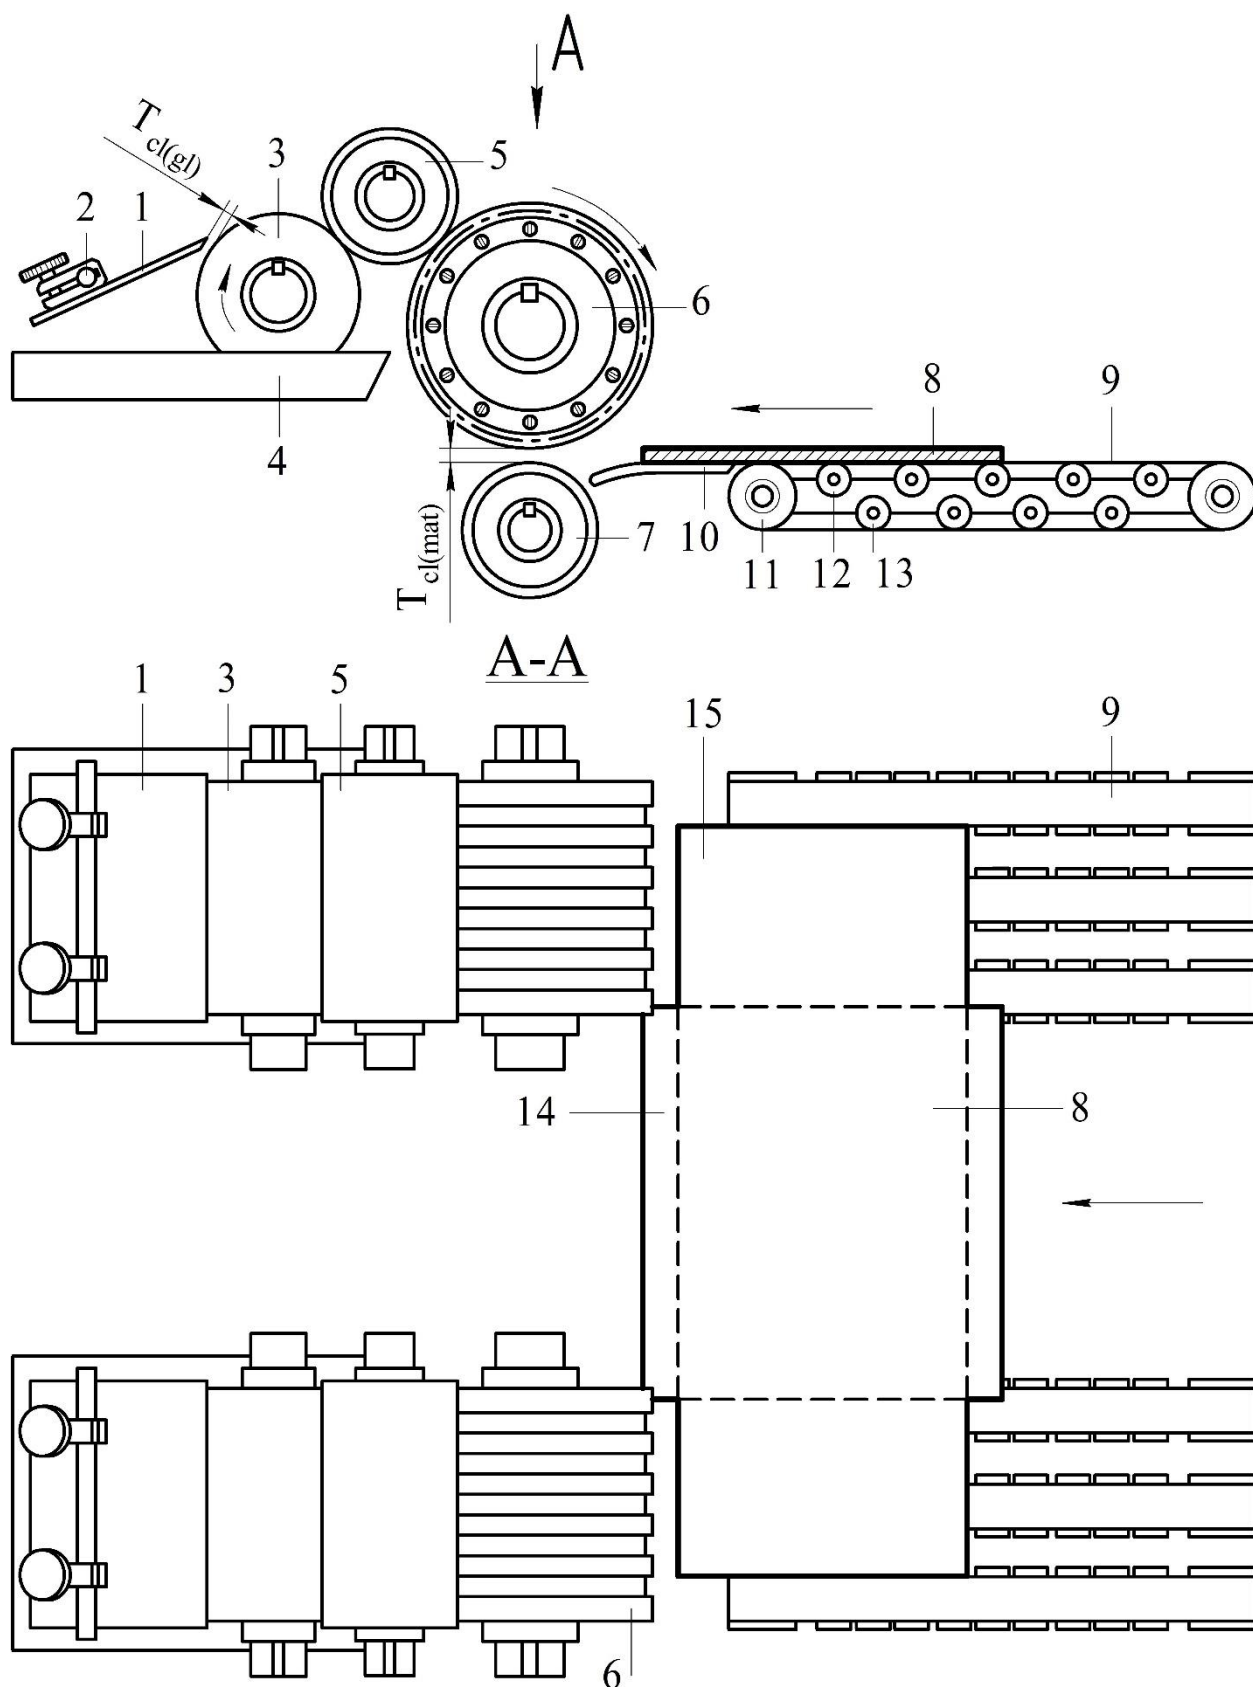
Клейовий апарат нанесення клею на клапани напівжорстких обкладинок, 1 – ракель регулювання шару клею; 2 – затискач ракеля; 3 – живильний клейовий вал; 4 – резервуар для клею; 5 – передавальний клейовий
